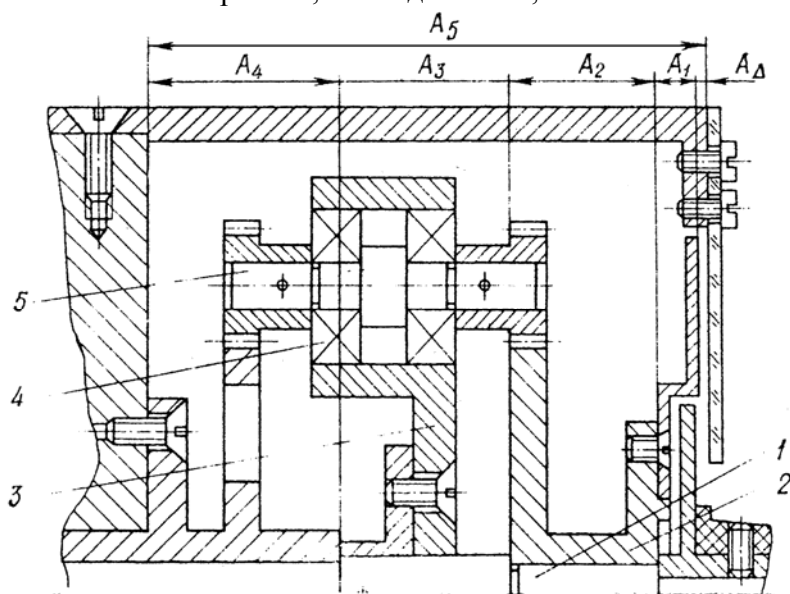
Узел подшипникового соединения: 1 – вал; 2 – колесо; 3- водило;
